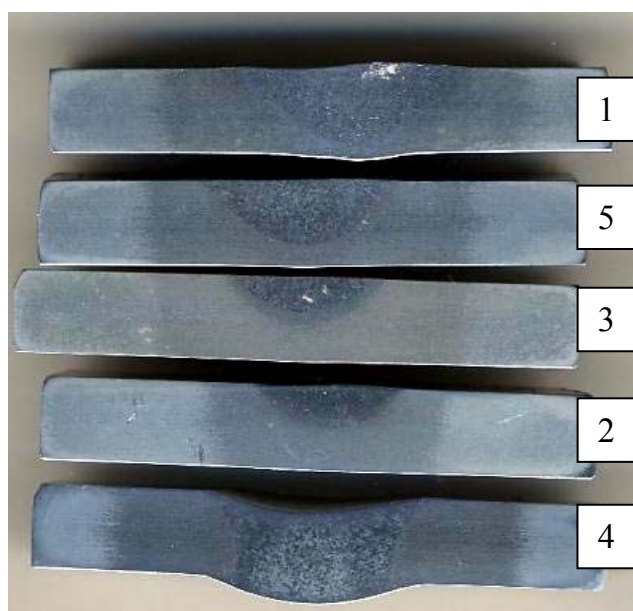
Macrographie des coupes transversales des échantillons d'aluminium 2017-T4 (d'ép. 5mm) à différents paramètres de soudage.
